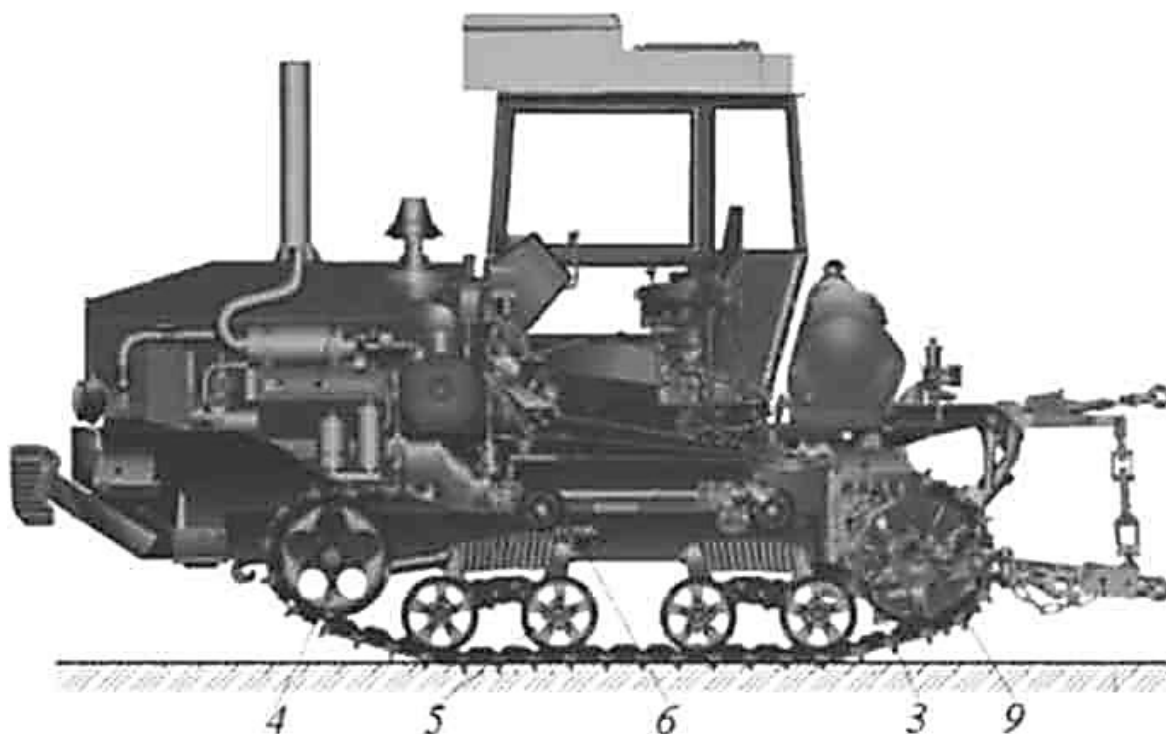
Схема расположения основных агрегатов и узлов гусеничного трактора
